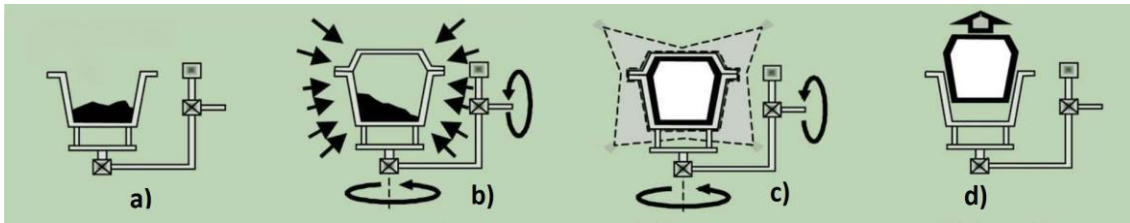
Etapas do processo de Rotomoldação [31].
